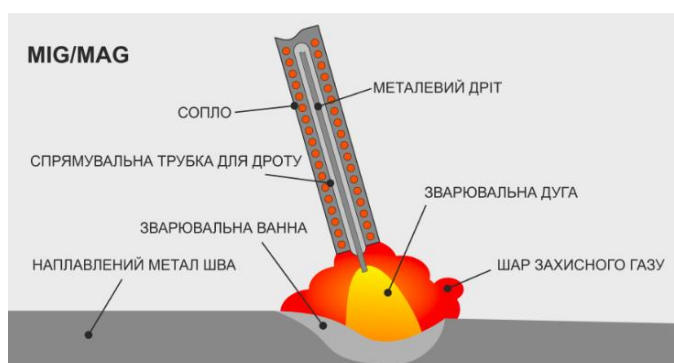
MIG-MAG (напівавтоматичне зварювання)
